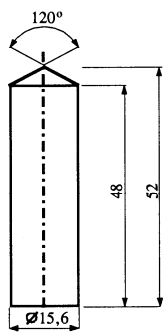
Цилиндрический бронзовый поршень; размеры в мм
